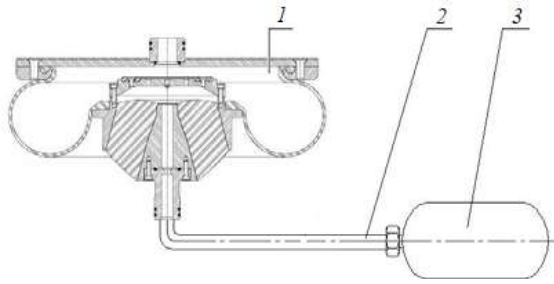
Схема пневматичної ресори з додатковим резервуаром
